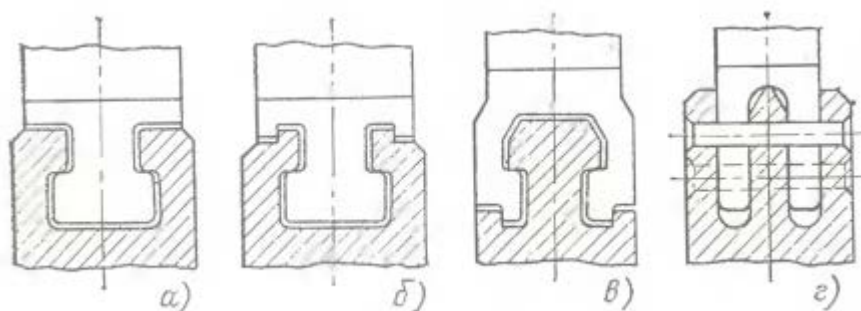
Хвостовики рабочих лопаток: а – Т-образный без заплечиков; б – Т-образный с заплечиками; в – грибовидный одноопорный; г – вильчатый
